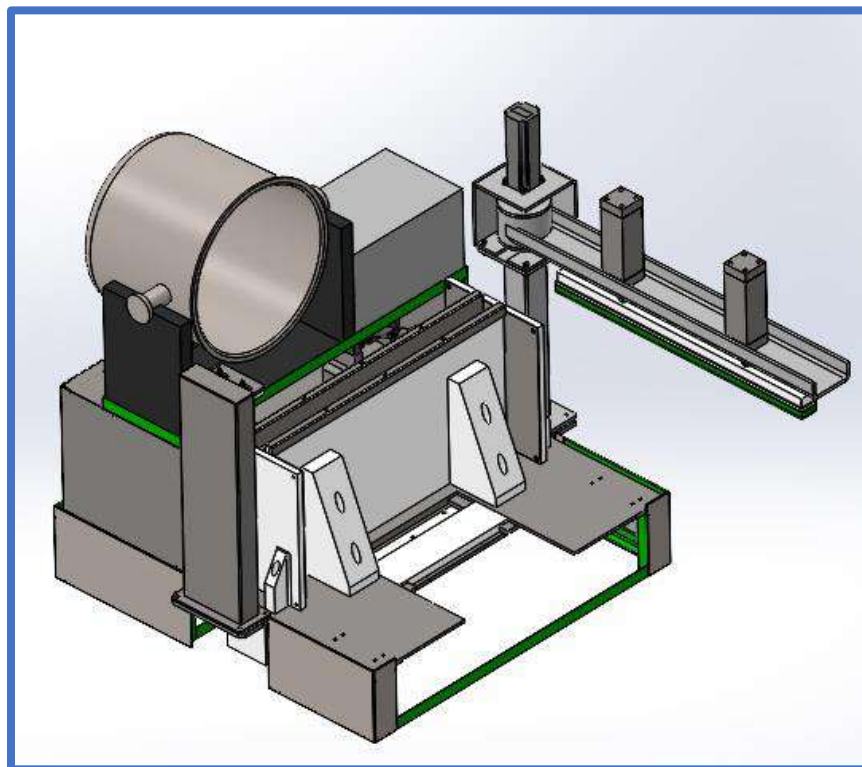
Máquina de hacer Bollos de Chipa y Amasadora
